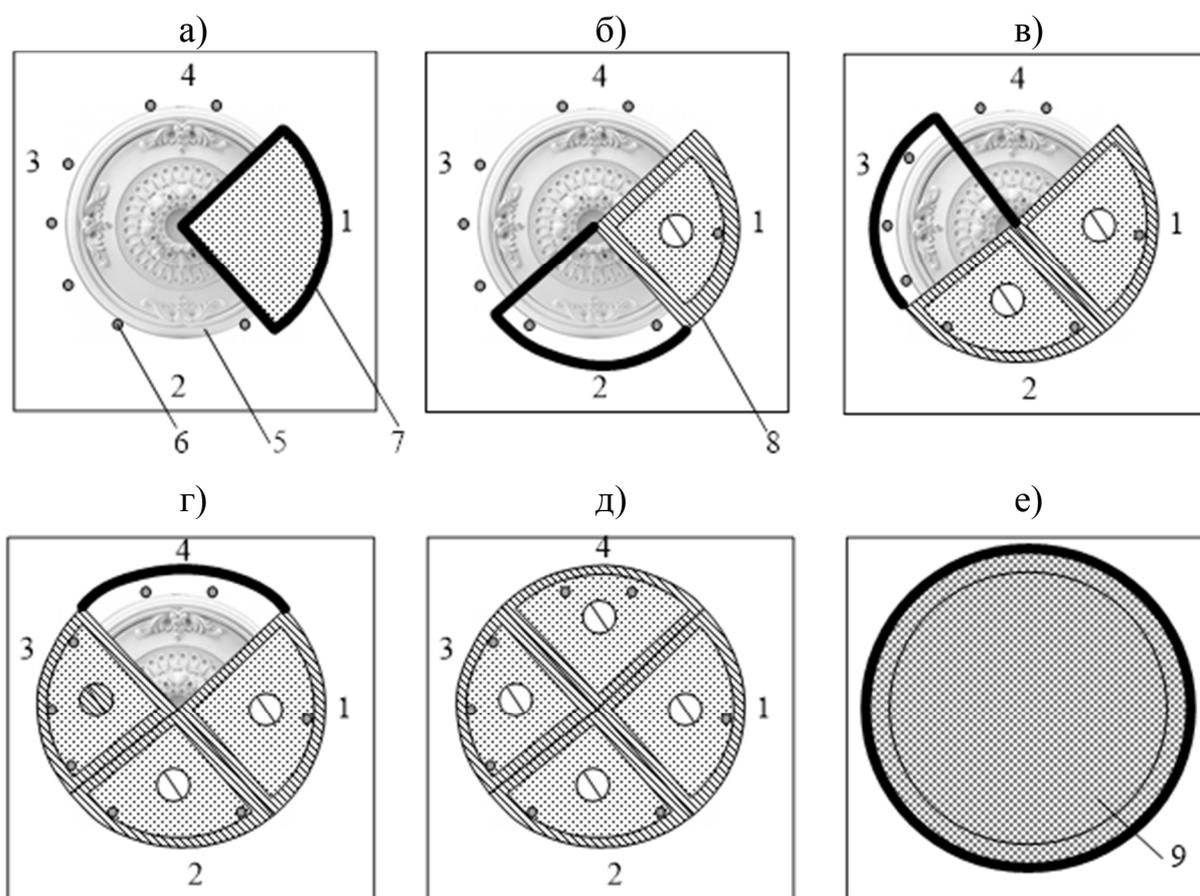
Изготовление сложной кусковой формы с розетки: а – подготовка модели и закладка первого куска; б – первый кусок с обрезанными кромками; в – отливка второго куска формы; г – отливка третьего куска формы; д – готовые куски формы с лунками и петлями; е – установка кожуха; 1–4 – куски; 5 – модель; 6 – лунки под замки; 7 – ограничители (опалубка); 8 – первый кусок; 9 – кожух
